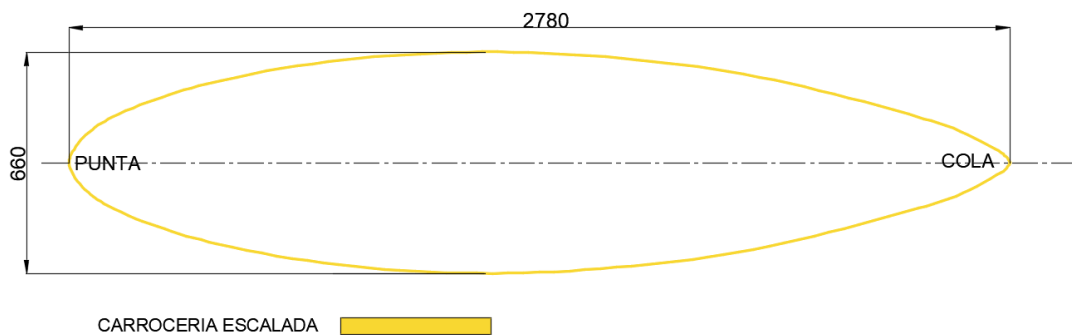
Dimensionamiento en milímetros (mm) de la vista superior del perfil aerodinámico seleccionado
